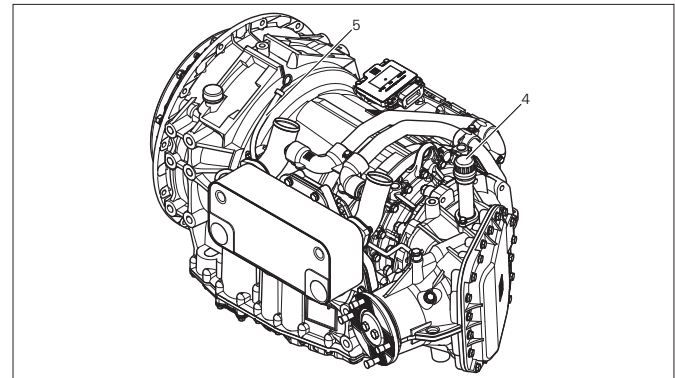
Коробка передач с угловым редуктором 80° LHD
